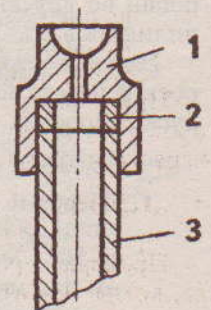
Способ увеличения длины штанги: 1 - наконечник; 2 - вставка; 3 - штанга
